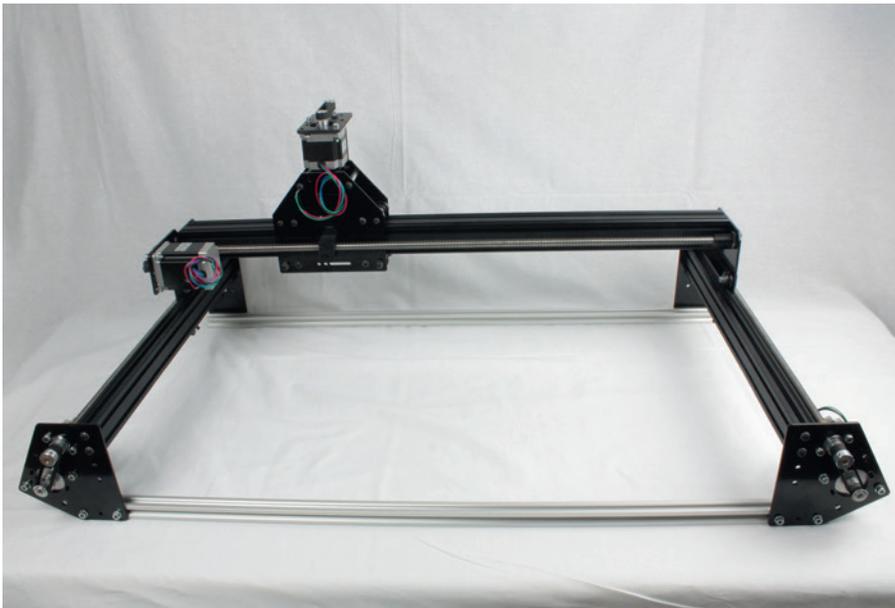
Der fertige mechanische Aufbau (hier noch ohne Arbeitsplatte)
